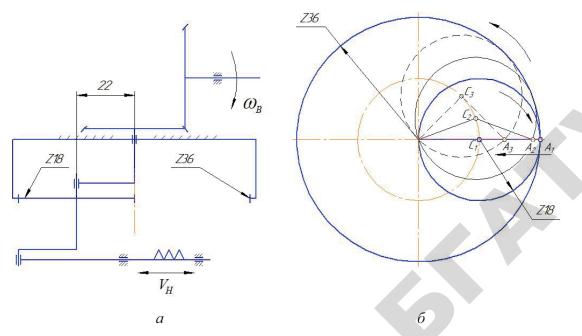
Кинематическая схема планетарного механизма (а) и фрагмент, обосновывающий движение ножа (б)
